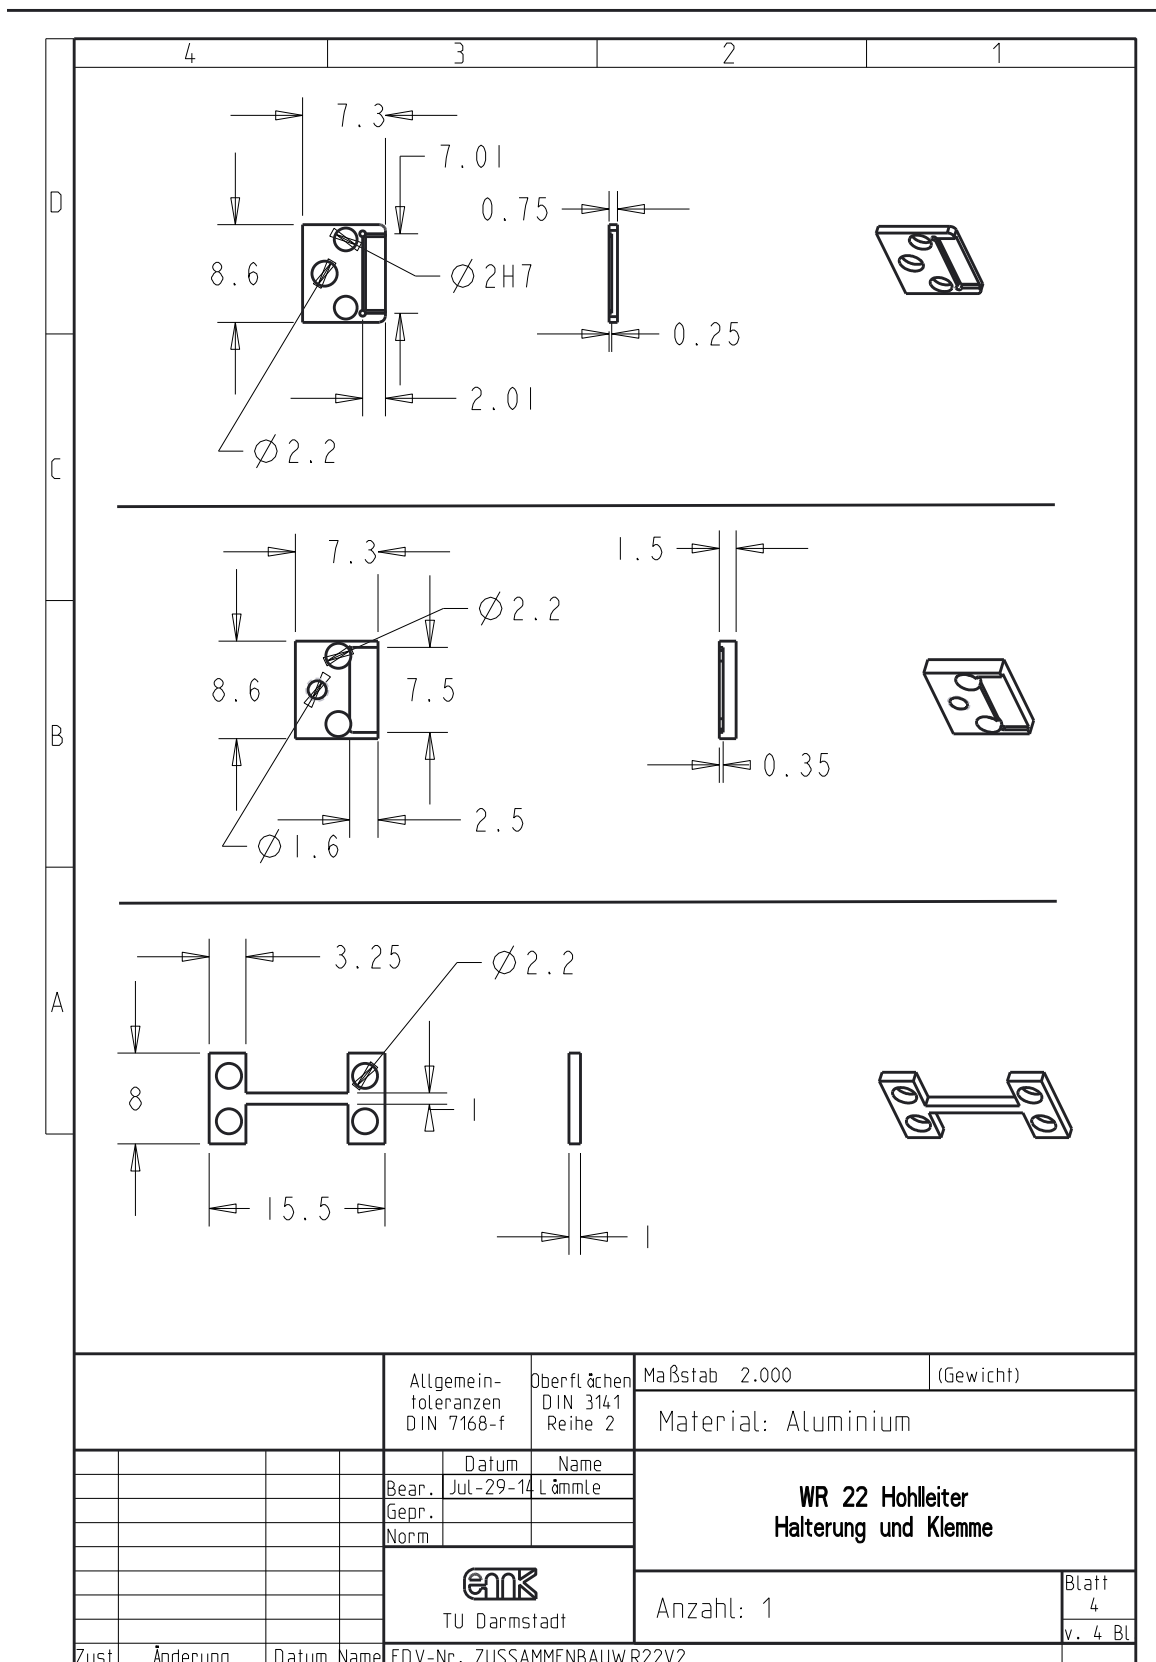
Technische Zeichnung des Splitblocks - 2. Version, Chiphalter
